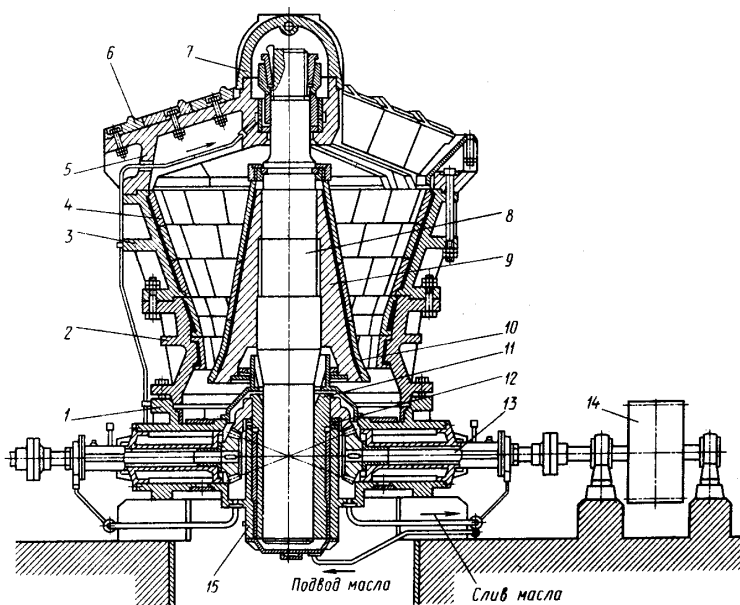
Конусная дробилка ККД-1500/180 крупного дробления.
